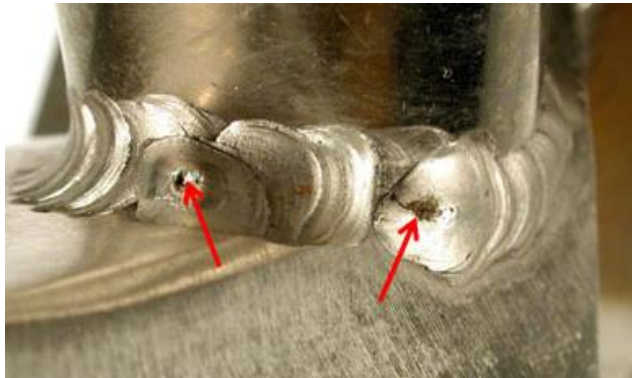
Fracturas en el cráter de los reinicios de la soldadura (30)
